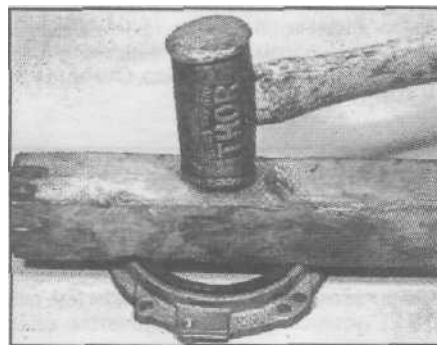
Установка новой задней манжеты коленчатого вала
